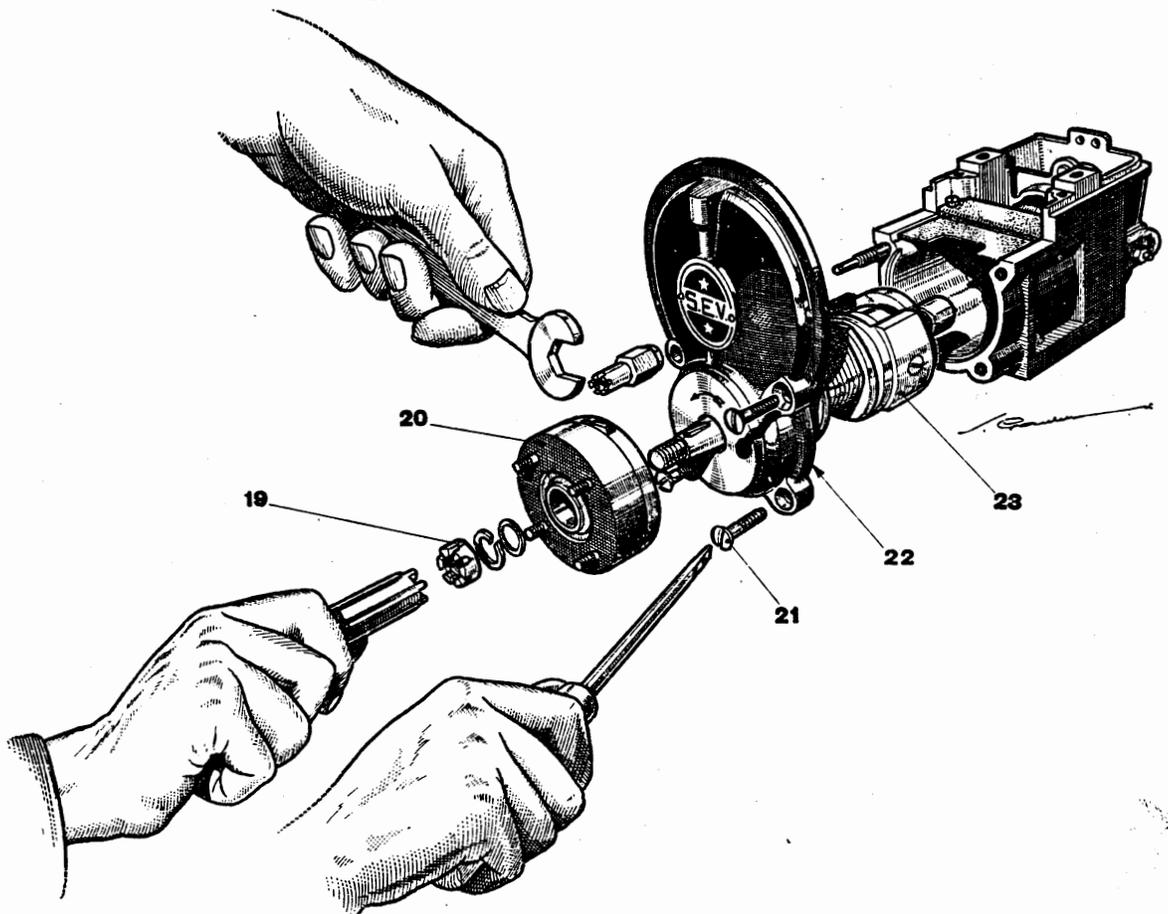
DÉMONTAGE DU DÉCLIC ET DU FLASQUE AVANT
